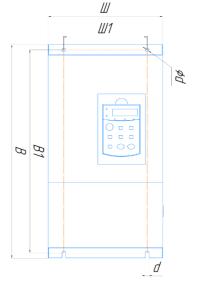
габаритные и установочные размеры устройств серии LCI в пластмассовом корпусе
